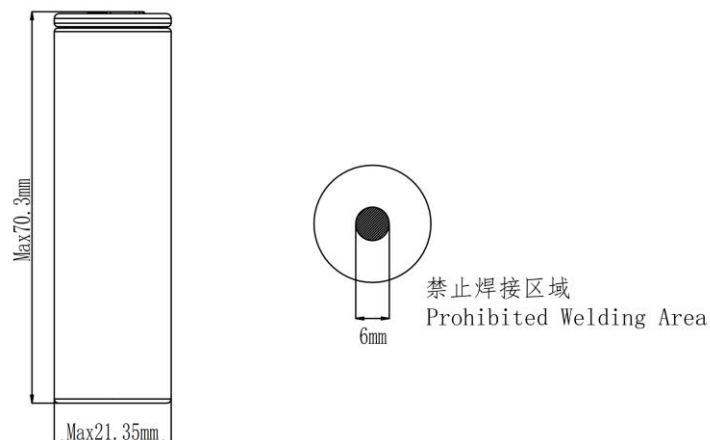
电芯尺寸(含套膜) Figure 1. Cell dimension with tube.
